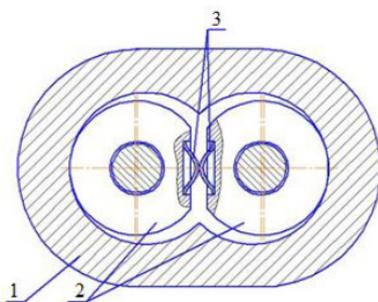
Конструкция опорных втулок НШ в сборе с упругими раздвижными элементами
